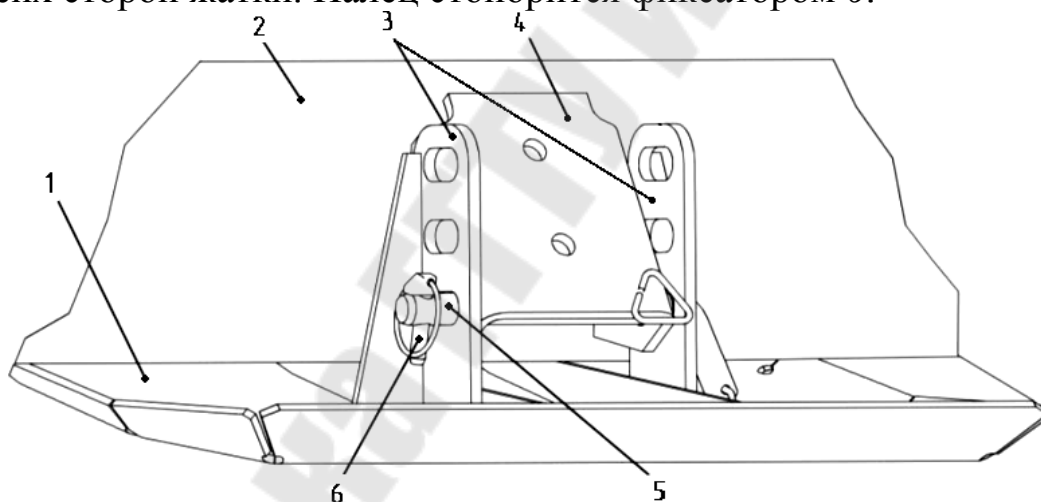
Схема регулировки высоты среза: 1 – башмак; 2 – рама; 3 – стойки; 4 – направляющая; 5 – палец; 6 – фиксатор
